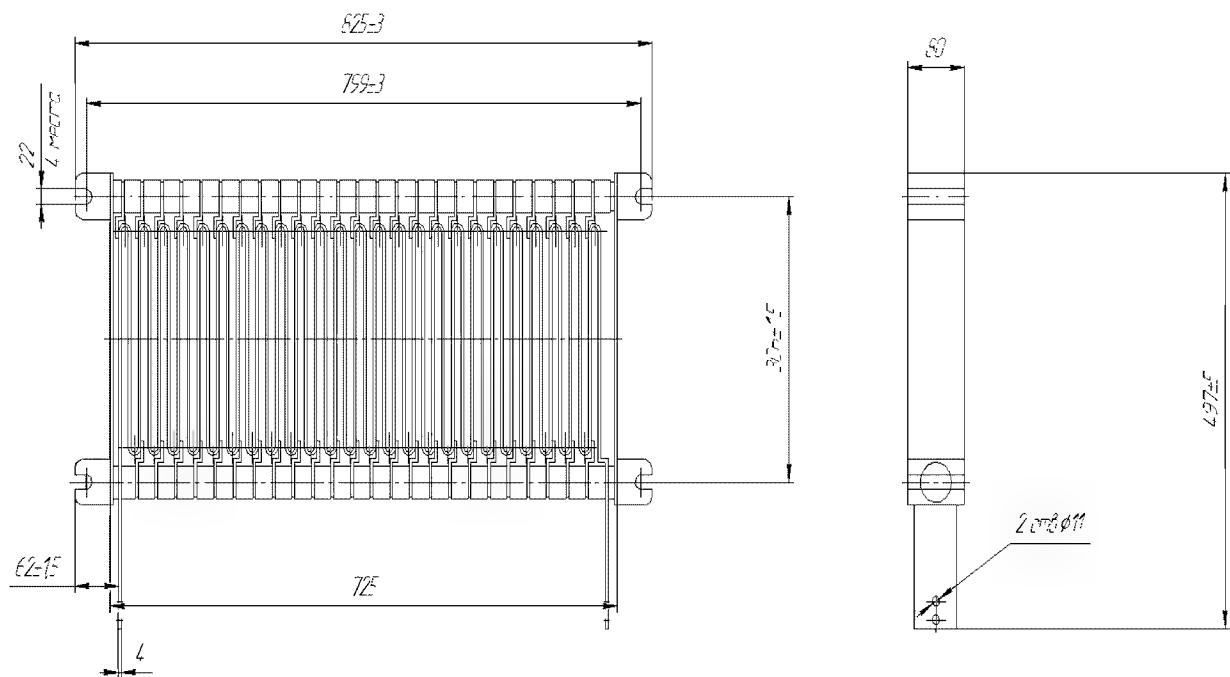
Габаритные размеры резистора типа РЛТ.
